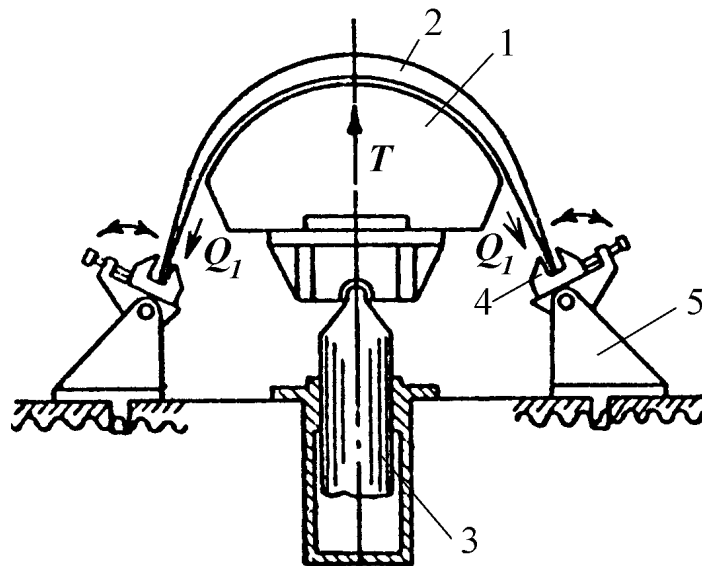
Схема гідравлічного обтяжного преса марки ОП: 1 – обтяжний пуансон; 2 – заготованка; 3 – силовий циліндр; 4 – самоустановлюваний затискач; 5 – траверса
